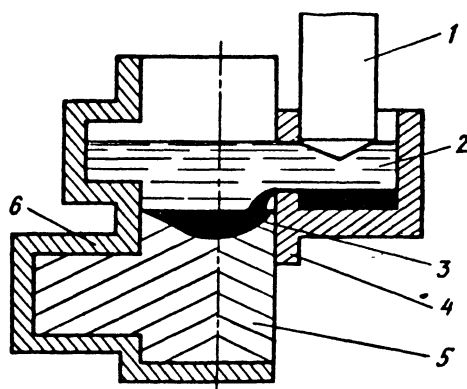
Схема ЭШП с переливом металла: 1 - расходуемый электрод; 2 - жидкий шлак; 3 - жидкий металл; 4 - плавильная емкость; 5 - отливка; 6 - литейная форма
